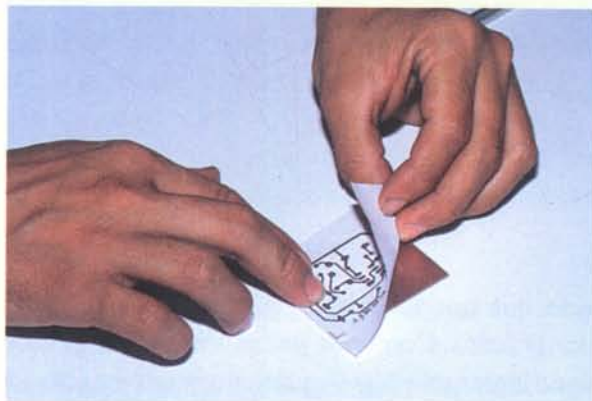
Se debe colocar el dibujo sobre la plaqueta
